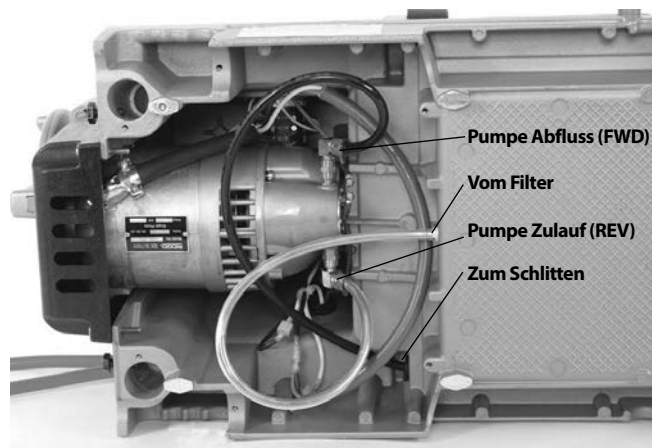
B – Ölpumpenanschlüsse für das Schneiden von Rechtsgewinden (Schalter auf FWD)
